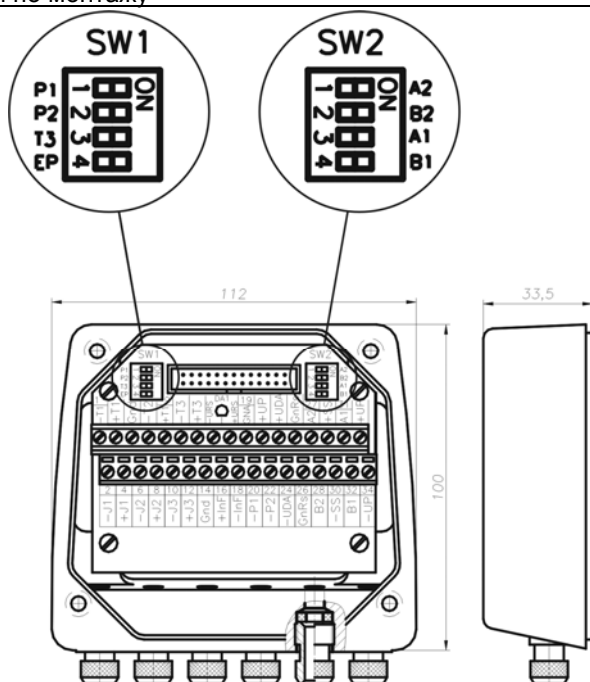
Габаритные и присоединительные размеры платформы подключения
